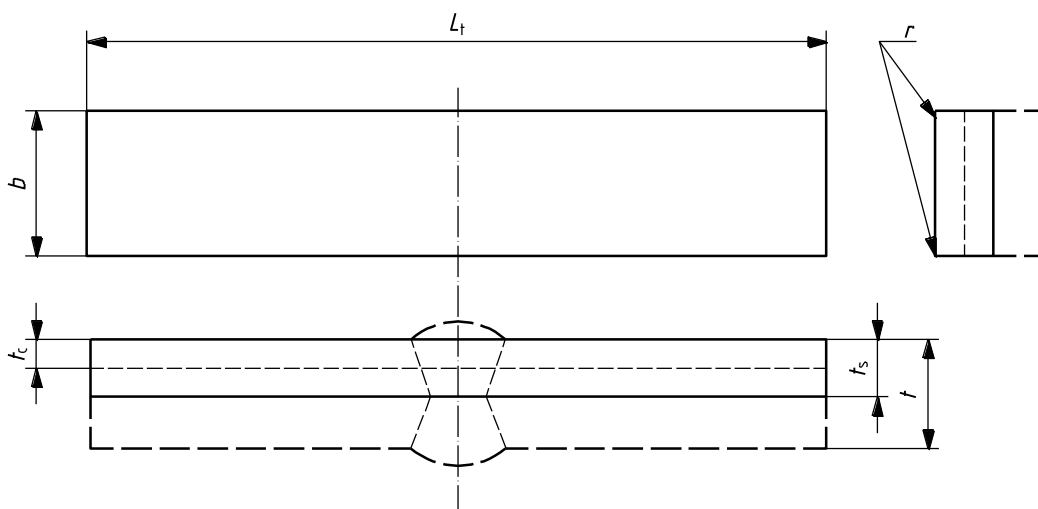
Образец для испытаний на загиб с растяжением лицевой стороны для плакировки со стыковым сварным швом (FBCB)
